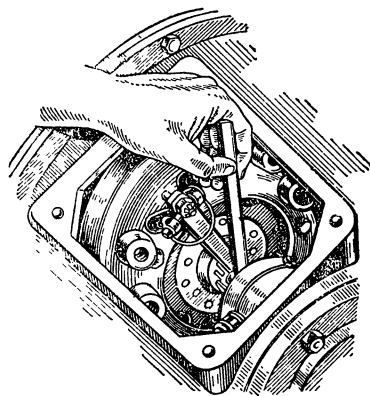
Проверка зазора между выступом отжимного рычага и кольцом (втулкой) отжимного подшипника
